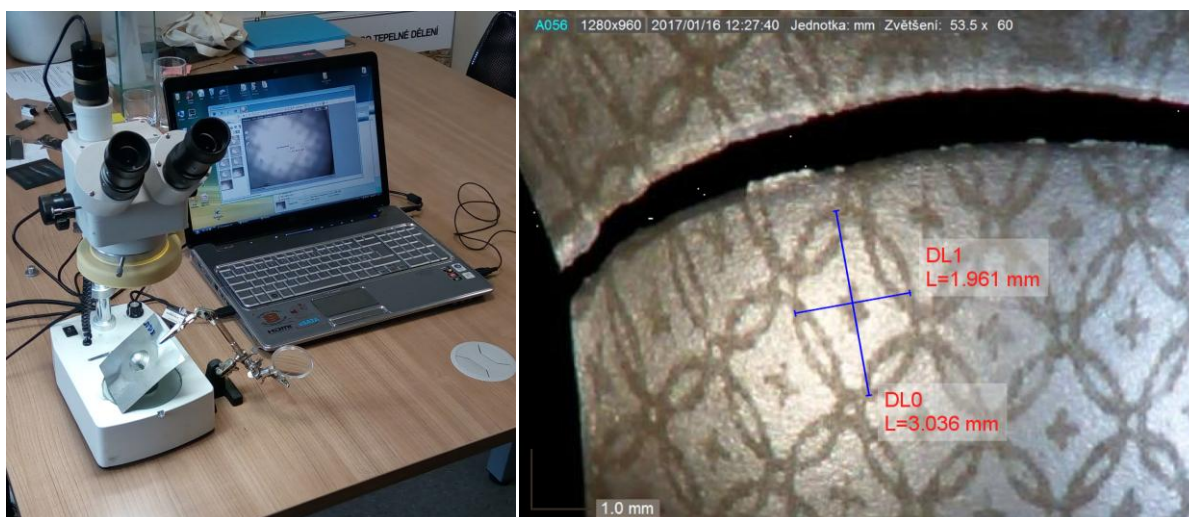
Geometrie vzorků po provedení Erichsenova testu
